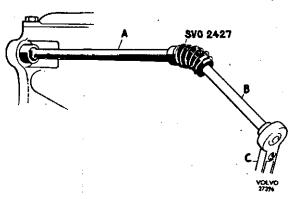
Ausbau der Getriebeschrauben, Wagen mit B 18-Motoren
